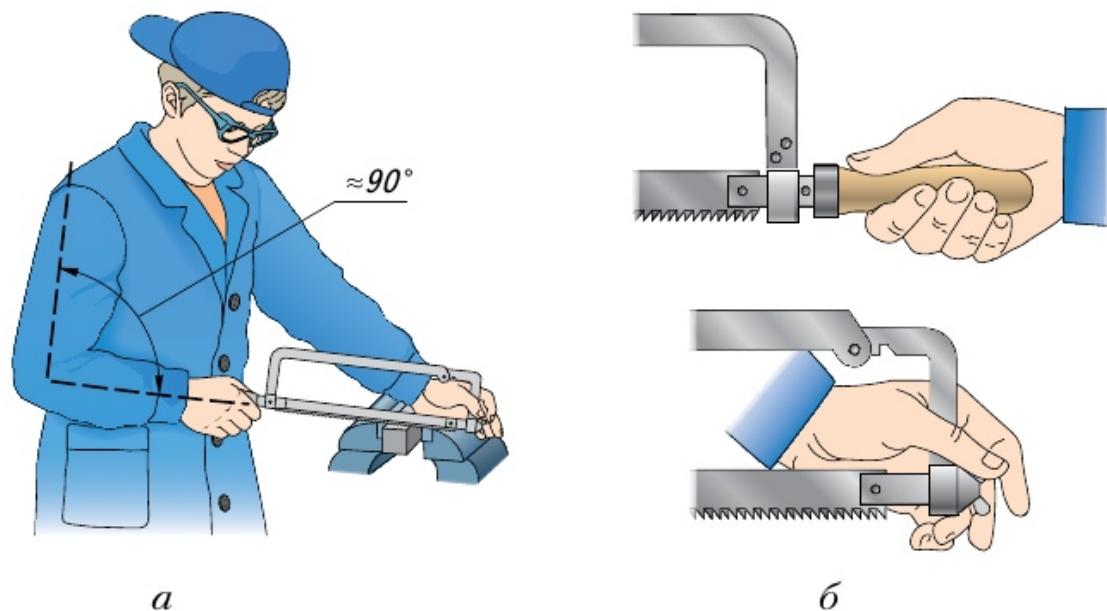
Работа ножовкой: *а* – положение корпуса; *б* – положение рук
